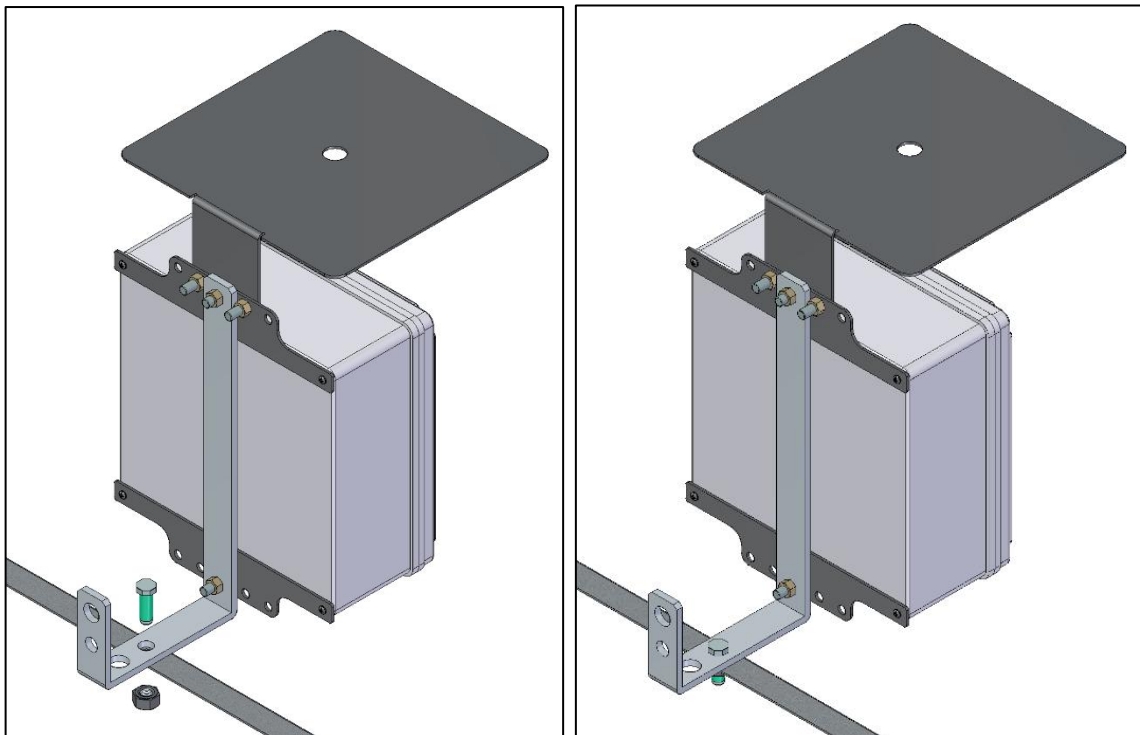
Fixação do GPS na face superior da viga do pivô.
